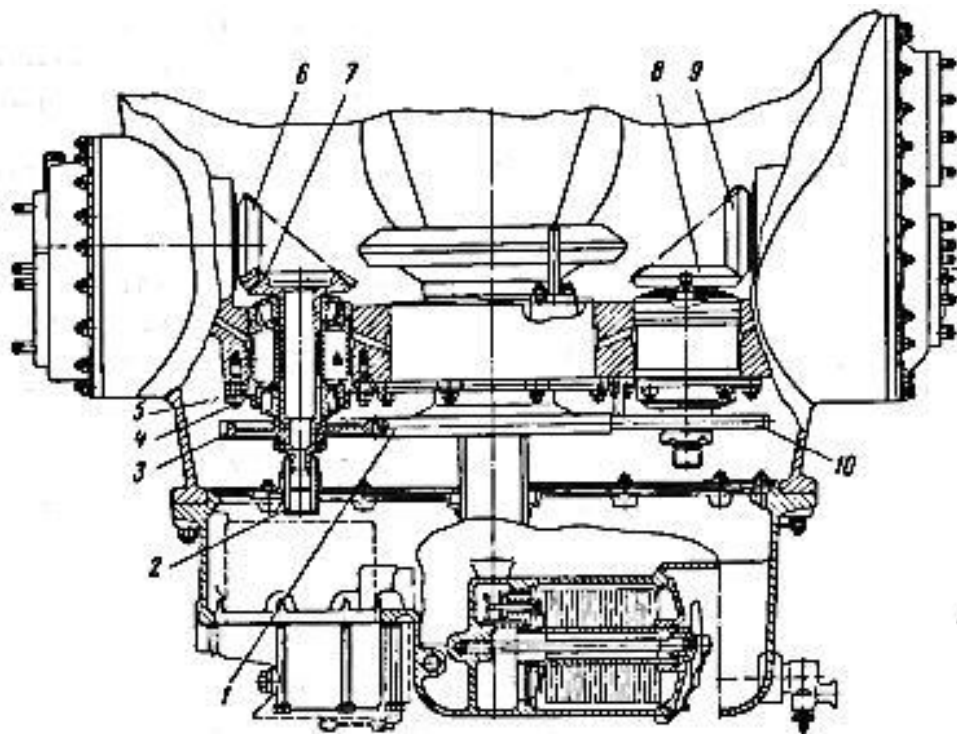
Поперечний розріз нижньої частини головного редуктора ВР-8:
